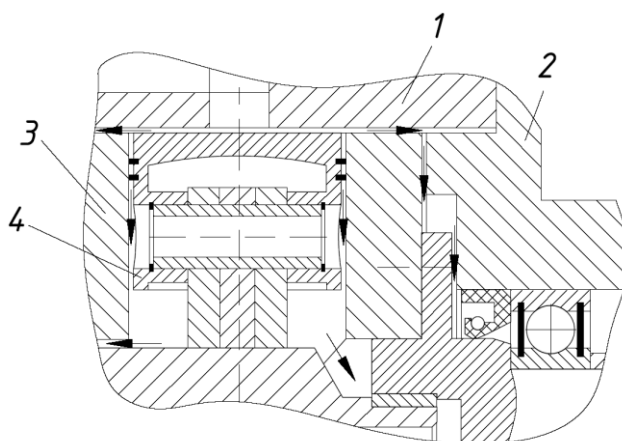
Схема втрат робочого тіла через нещільності сполучних деталей: 1 – корпус двигуна; 2 – фланець (кришка); 3 – центральний ротор; 4 – поршень
